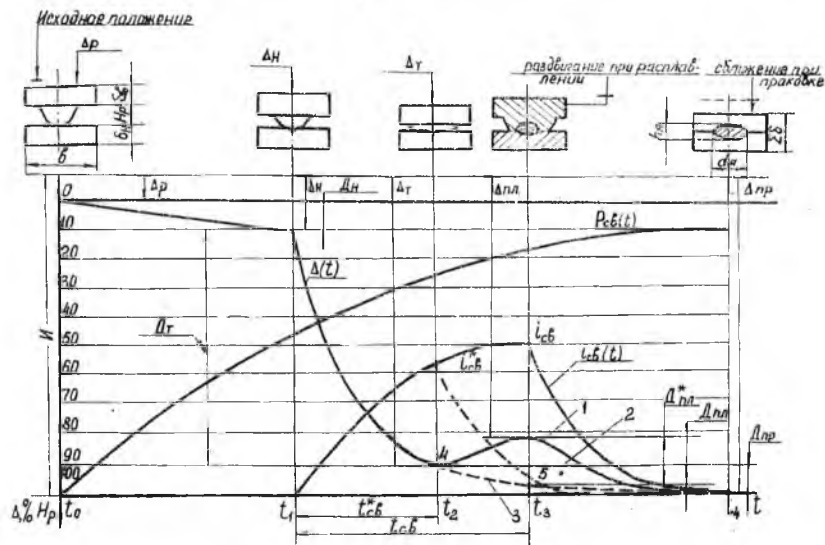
Циклограмма рельефной сварки и стадии деформации сварочного контакта:
